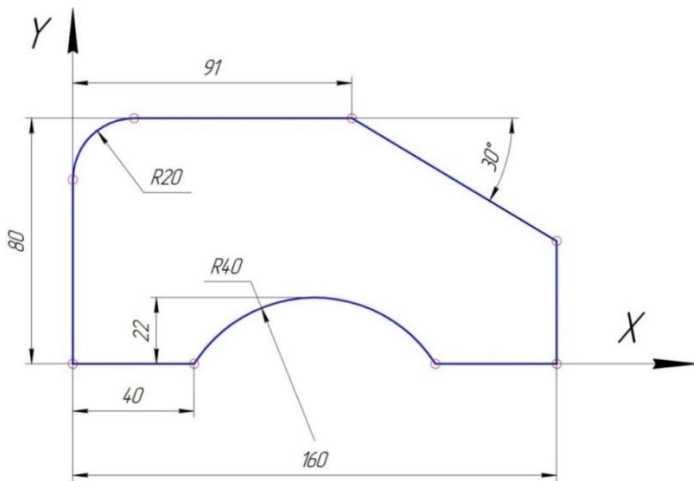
Опорні точки деталі під час фрезерного оброблення
